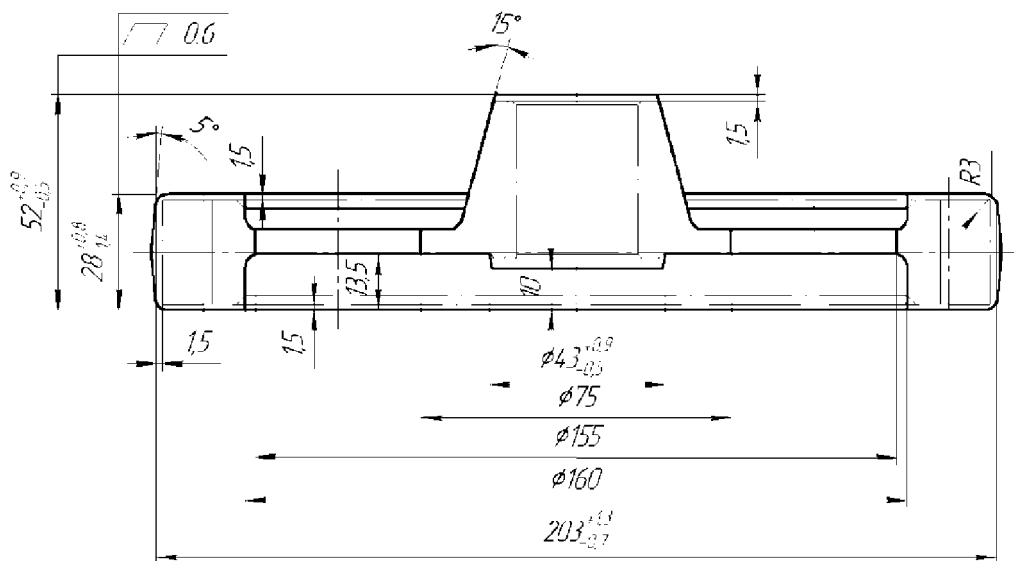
Ескіз заготовки деталі «Зубчасте колесо»
